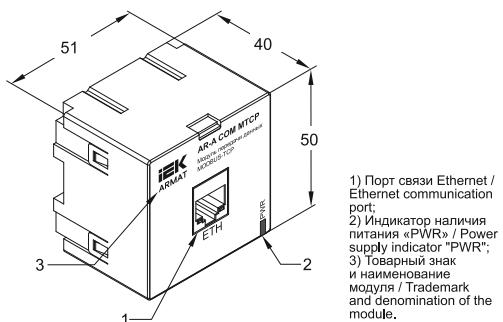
Габаритные размеры и внешний вид модуля передачи данных / Figure 1 – Overall dimensions and appearance of the communication module
